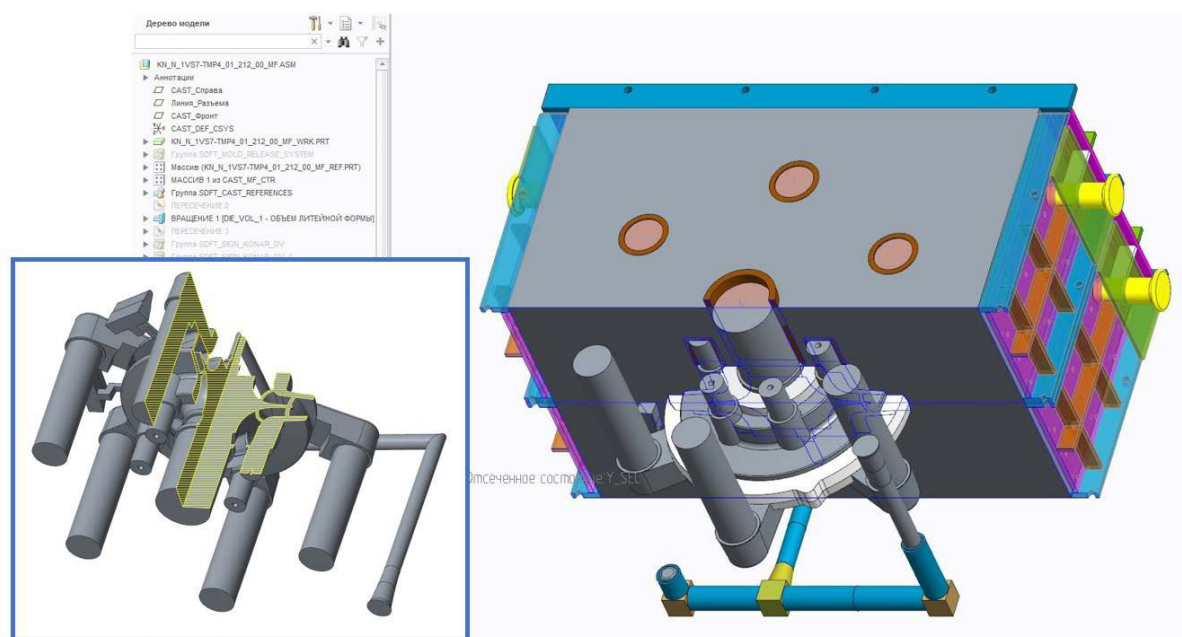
Общий вид 3D-моделей сборки основной литейной формы и результата литья
